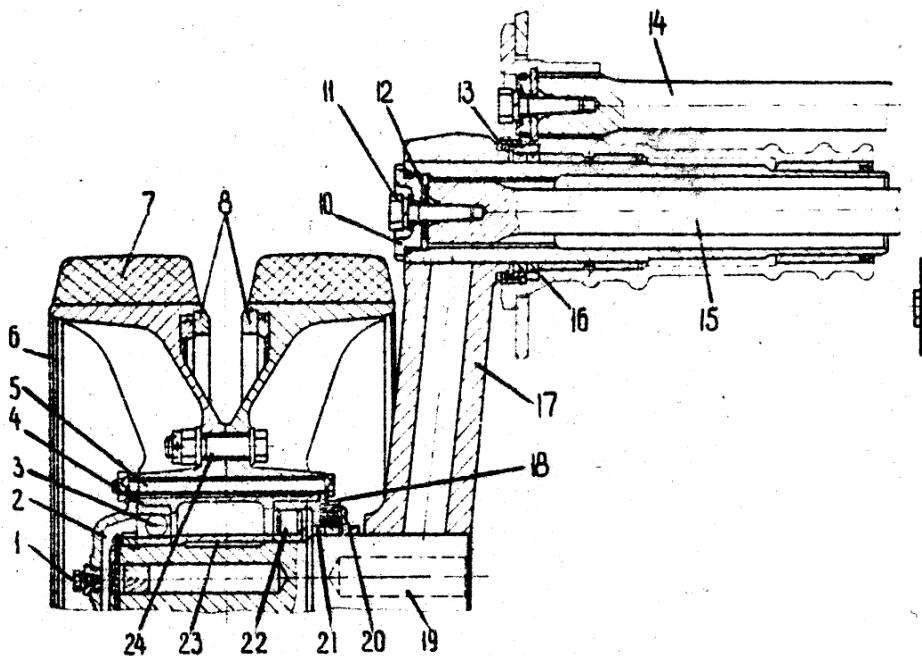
Опорний коток з торсійною підвіскою:
